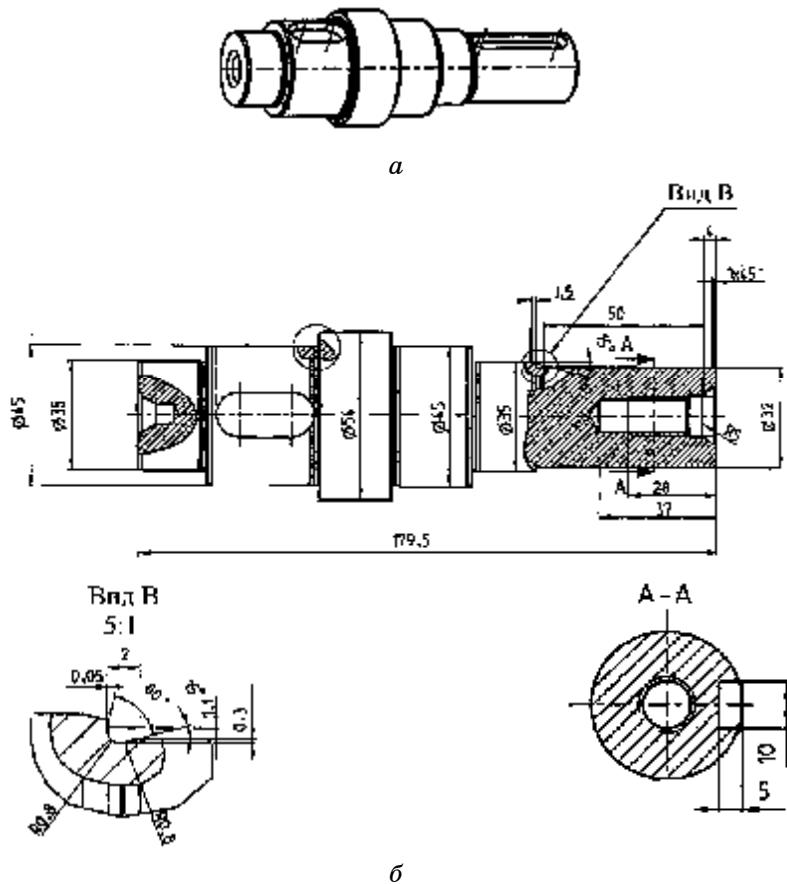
Загальний вигляд (а) та креслення (б) вала привода компресора ВВП-5/8
